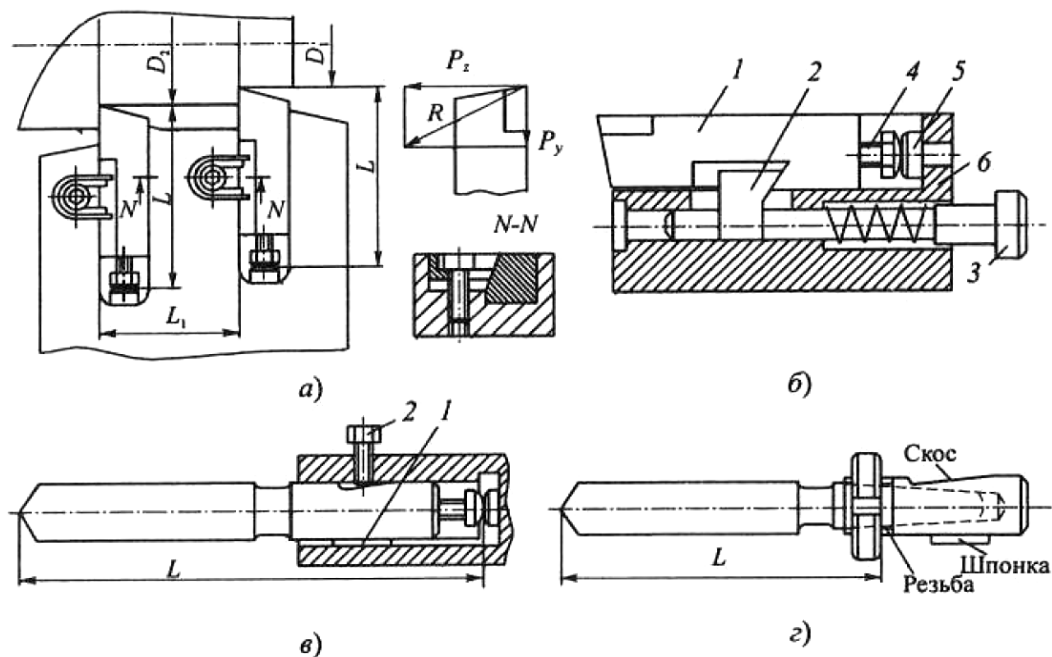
Устройства для бесподналадочной замены: а, б - резцов; в, г - осевых инструментов
